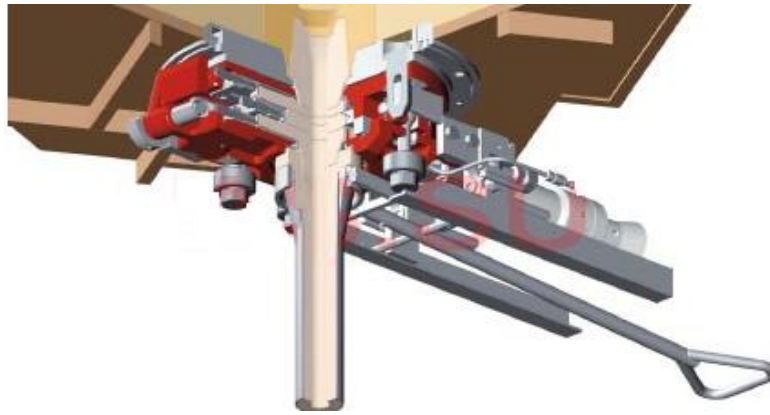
Схема подачі стали з ПК через трехплітний шибєрний затвор
